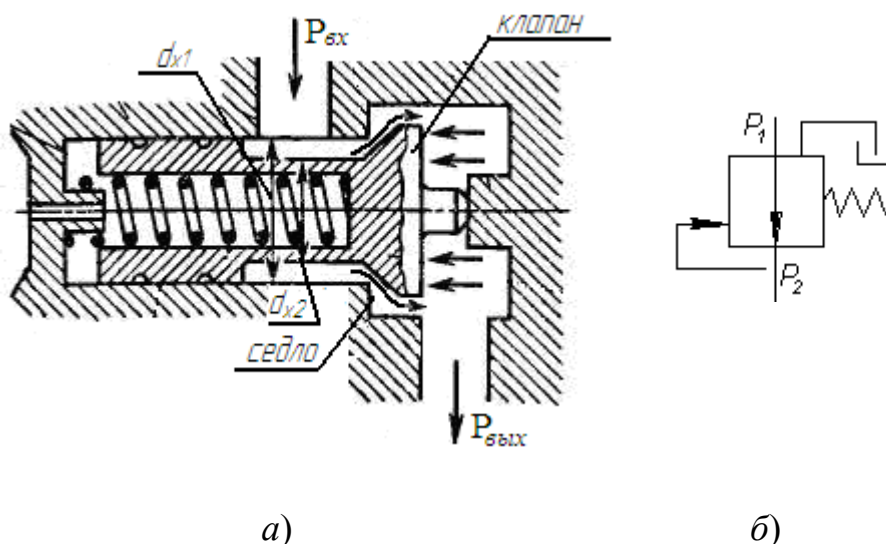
Редукционный клапан: а – конструкция клапана; б – графическое изображение
